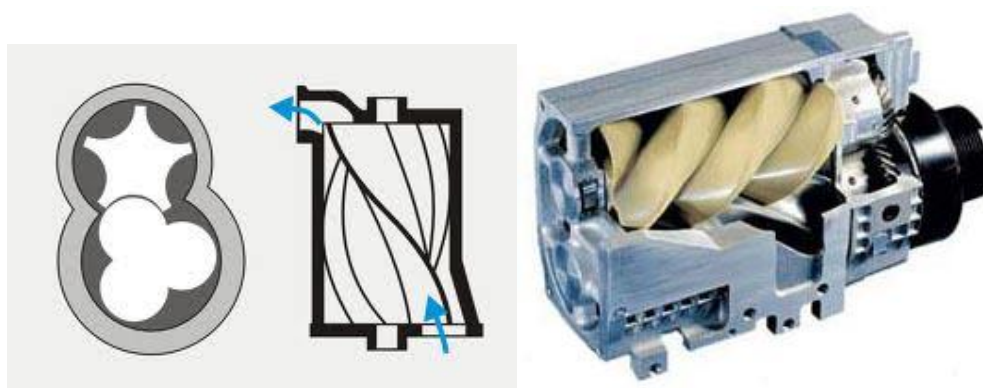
Схема нагнетателя конструкции Лисхольм
